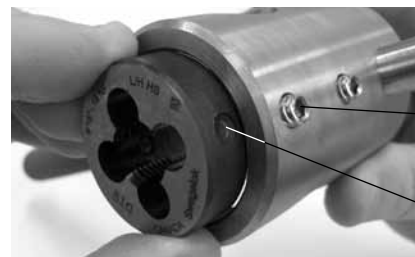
Ausrichten der Senkbohrungen für den Gewindeschneidkopf
